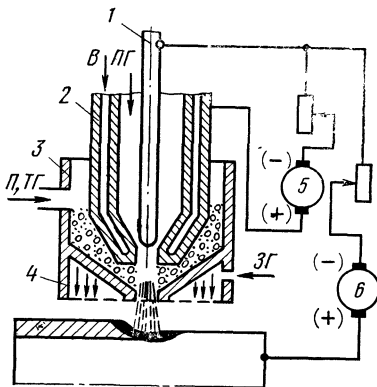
Схема плазменно-порошковой наплавки: *В* — вода; *ПГ* — плазмообразующий газ; *П* — порошок; *ТГ* — транспортирующий газ
